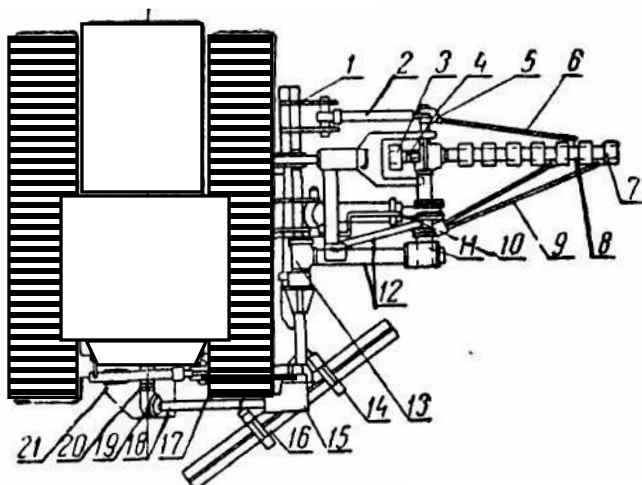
Каналоочиститель со скребковым рабочим органом: 1 – рама; 2, 10, 21 – гидроцилиндры; 3 – скребки; 4 – ведущая звездочка; 5, 12, 18, 20 – валы; 6, 9 – растяжки; 7 – натяжной ролик; 8 – рама рабочего органа; 11, 13, 15, 19 – редукторы; 14 – гидроцилиндры; 16 – кавальероразравниватель; 17 – базовая машина
